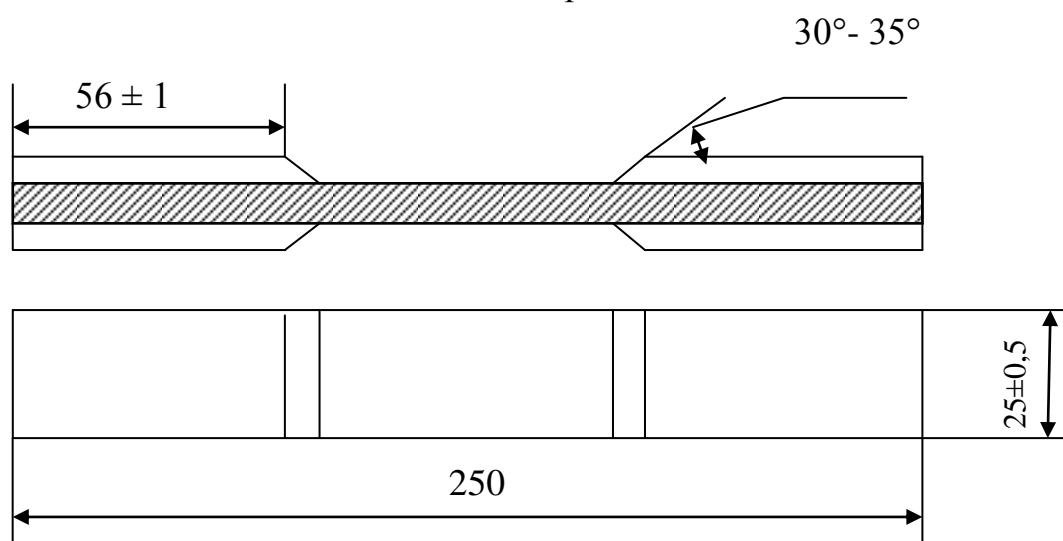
Форма и размеры образца для испытания стеклопластика на растяжение
